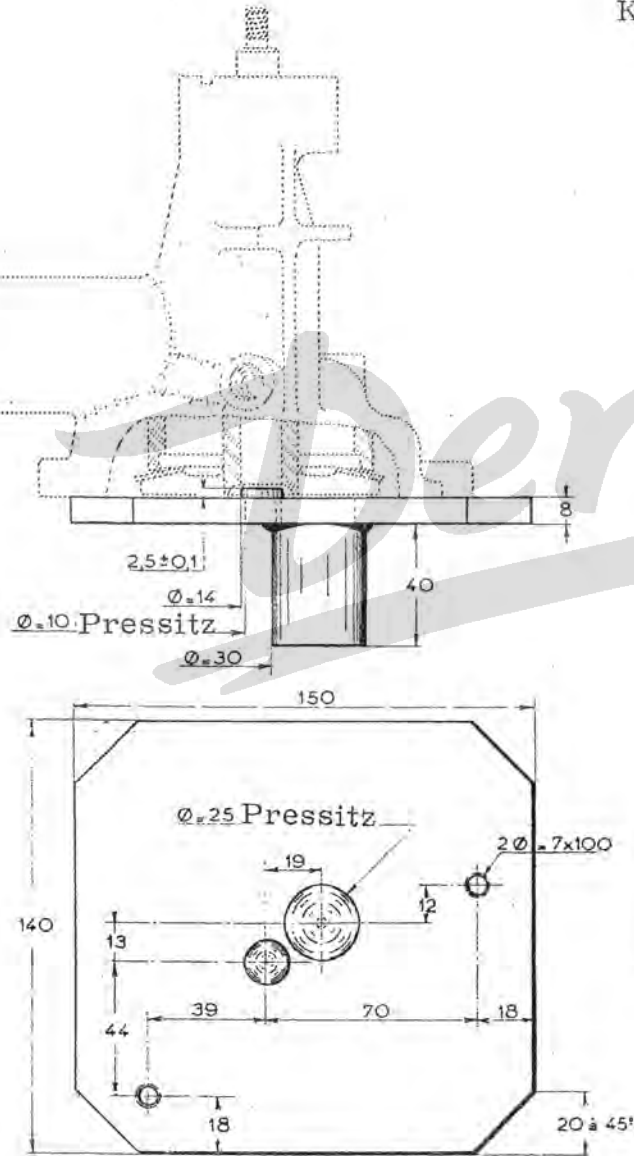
Schlüssel für Mutter am Kugellager der Pumpe 1634-T
